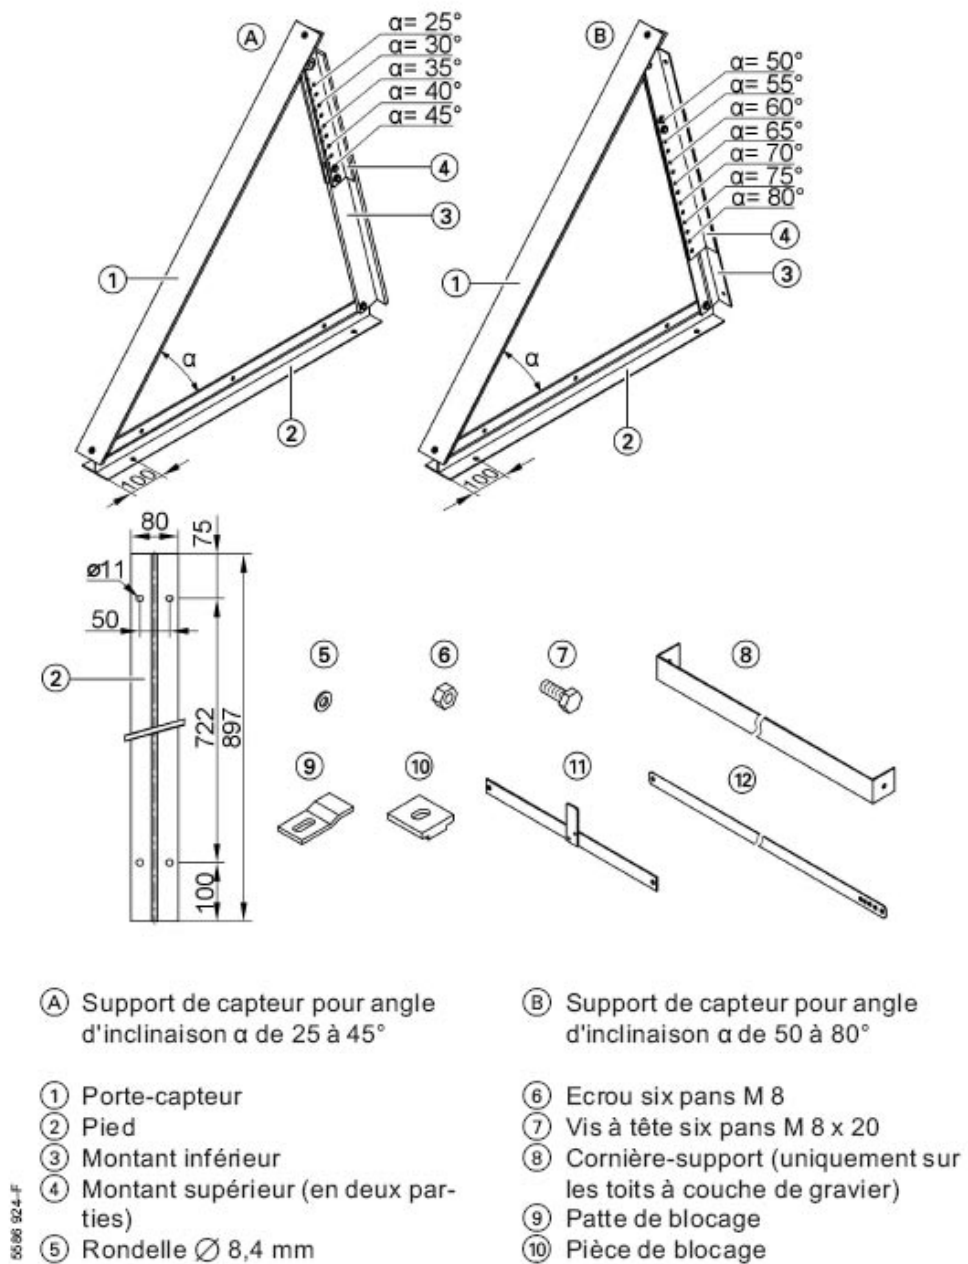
Accessoire pour montage sur toiture-terrasse (version SH1)
